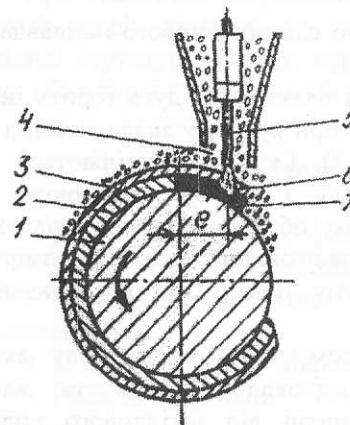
Схема автоматичного наплавлення під флюсом:
